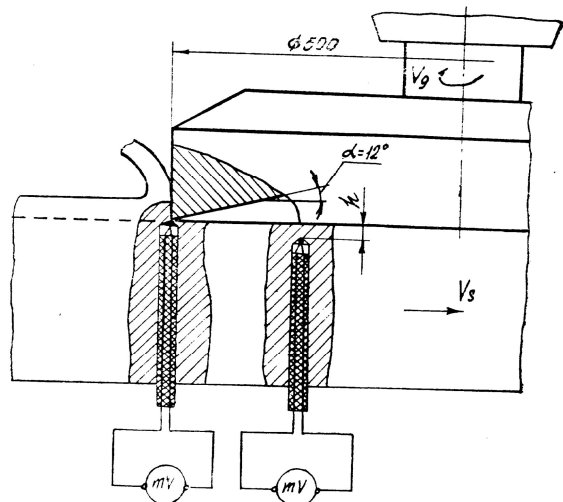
Схема установки термопар для измерения температуры поверхности обрабатываемой детали
